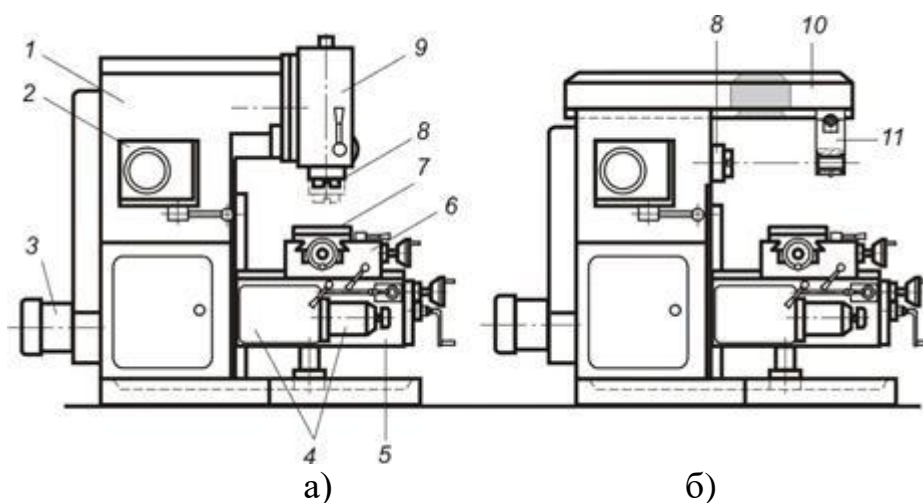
Схемы компоновок вертикально-фрезерного (а) и горизонтально-фрезерного (б) станков
